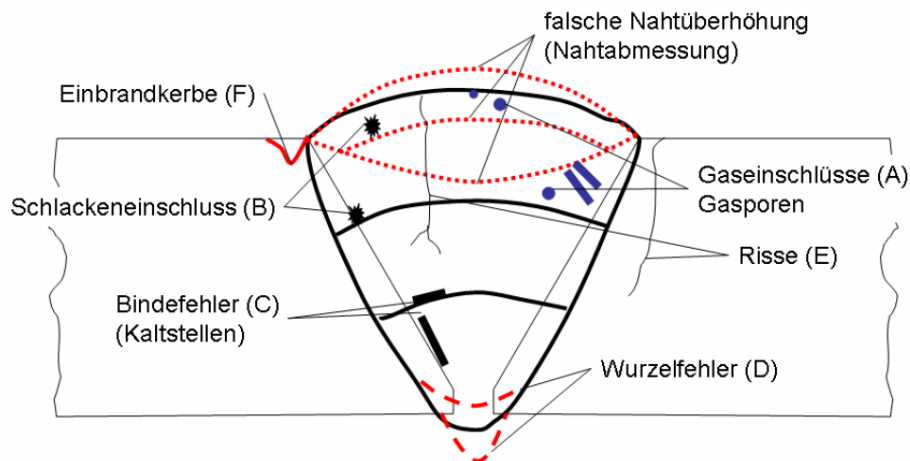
Schweißnahtfehler im Querschnitt einer Stumpfnah (V-Naht, 60° Öffnungswinkel) [12]
